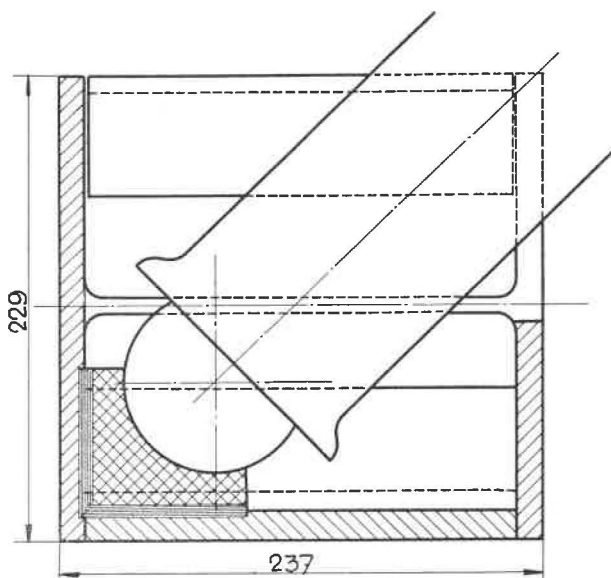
Bout de poutrelle. Amarrage tête de taille.
